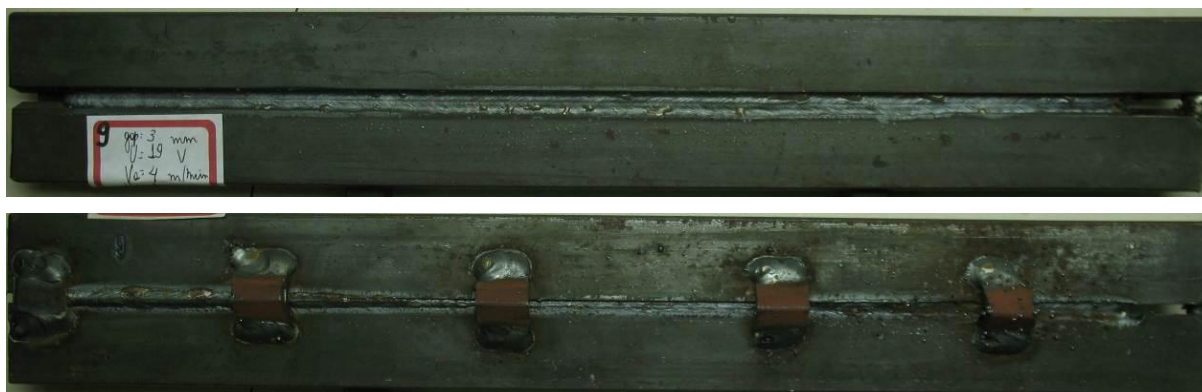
Teste 9 (face e raiz) (largura de cada chapa é 25 mm)
